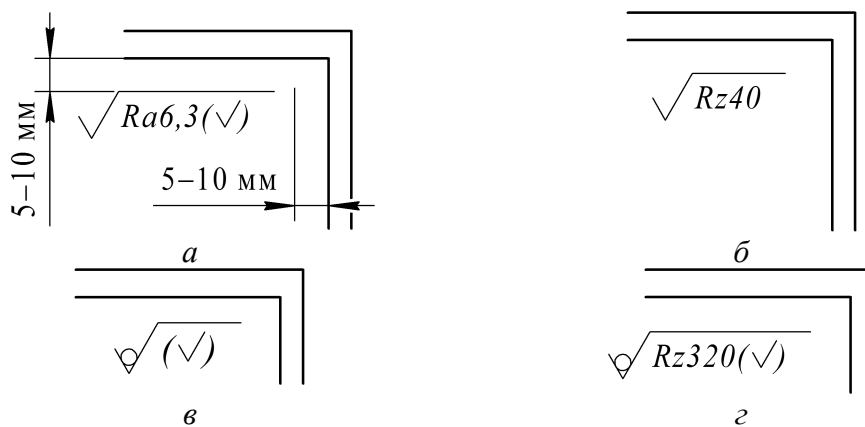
Обозначение одинаковой шероховатости на чертежах
